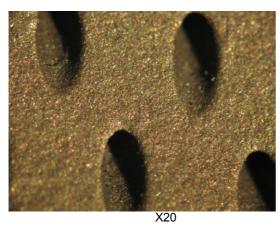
Внешний вид перфорационных отверстий на поверхности лопатки ТВД из сплава ЖС32ВИ с покрытием СДП-2.
